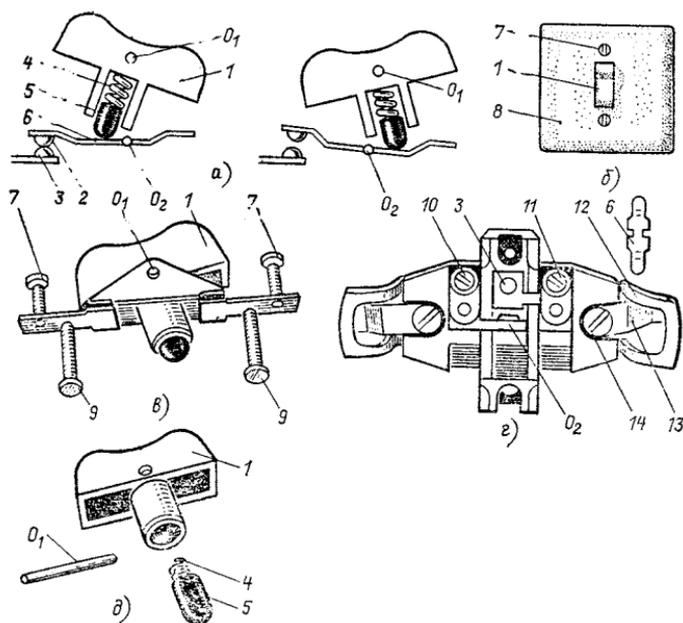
Выключатель с клавишным приводом для скрытой установки:
